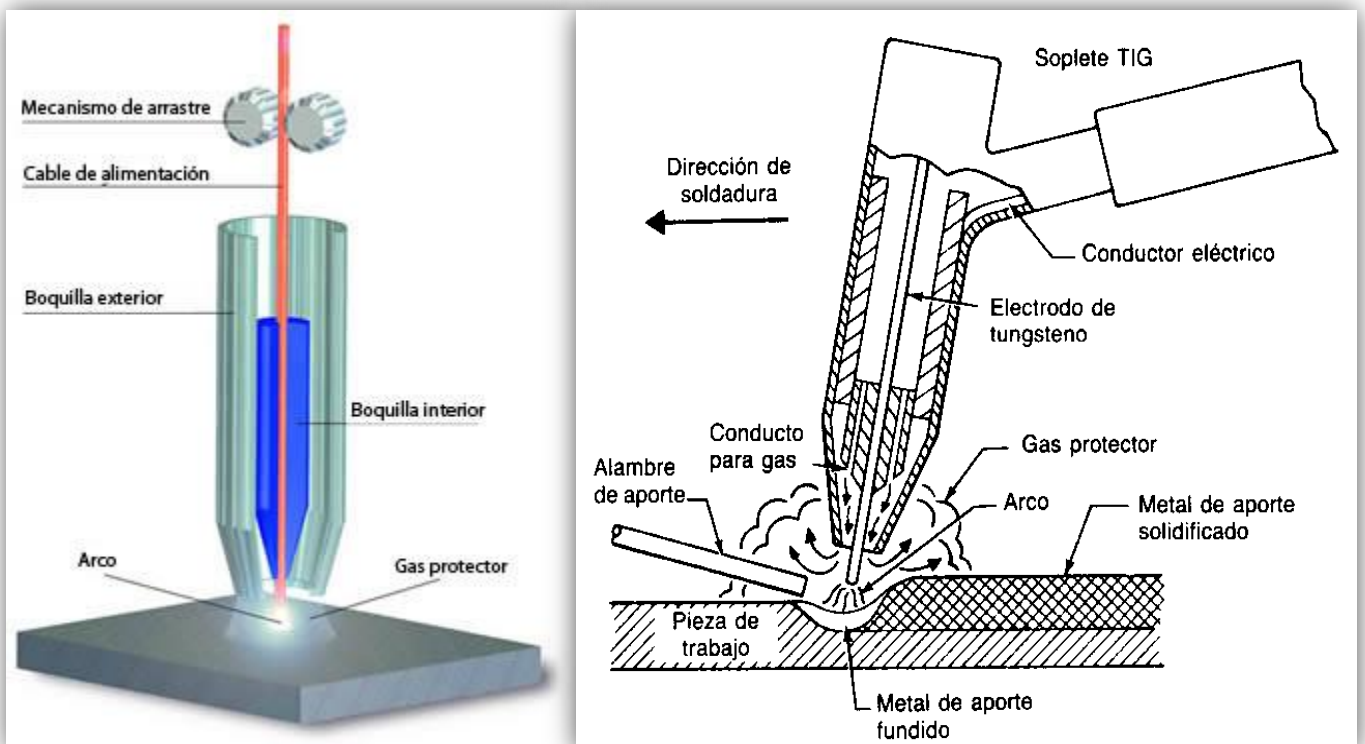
Proceso de Soldadura MIG/MAG
